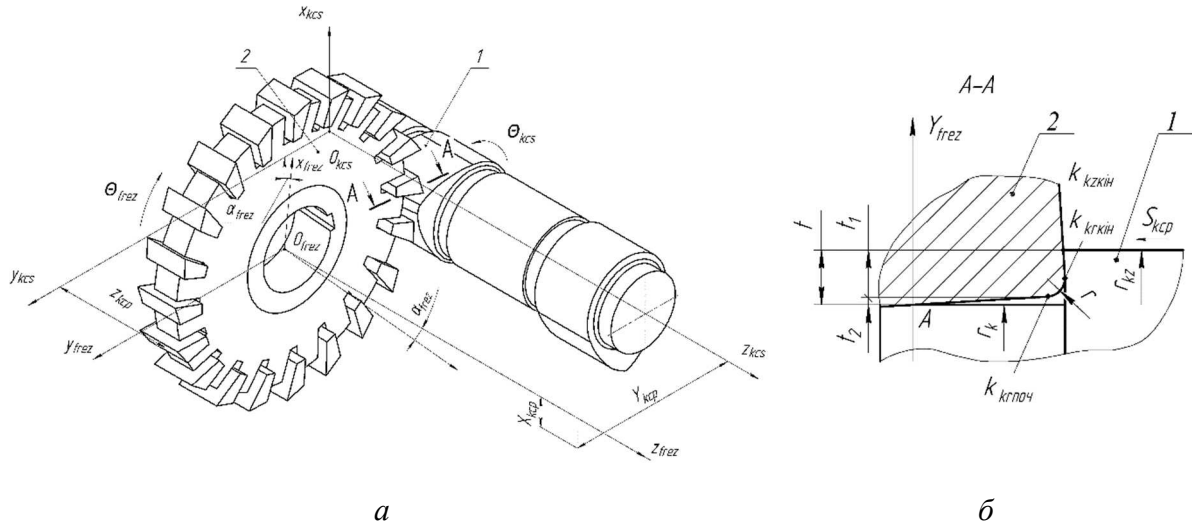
Схема фрезерування кулачка розподільного вала зі схрещеними осями інструмента та деталі
